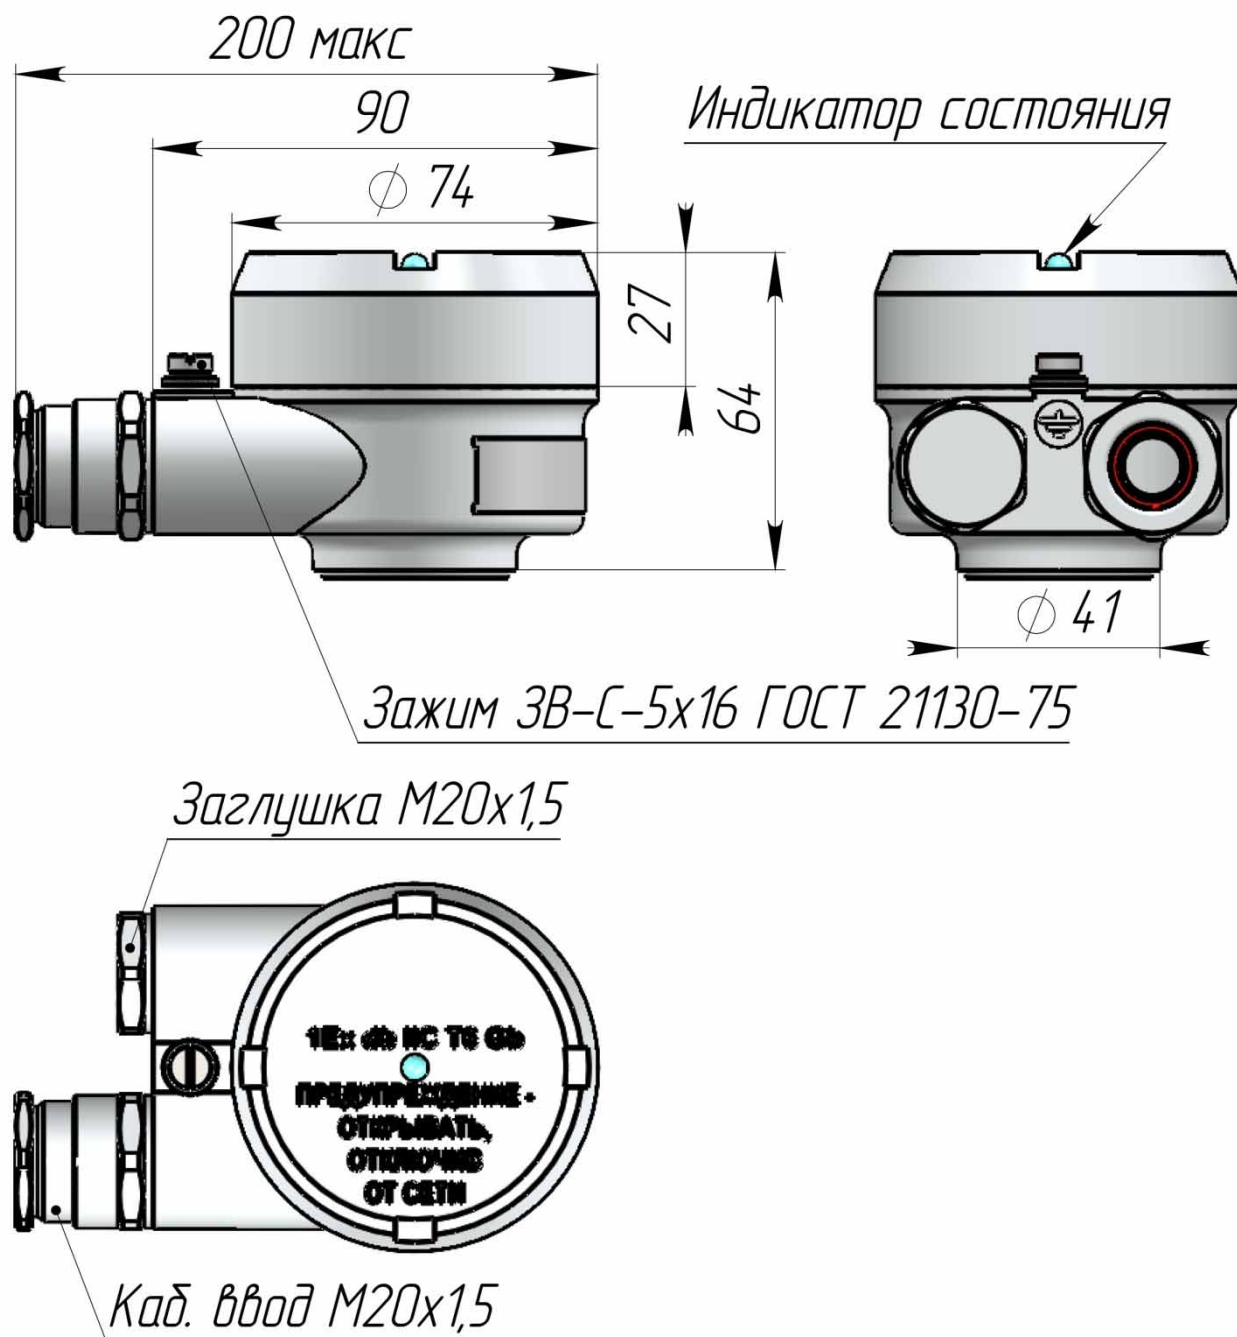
Габаритные размеры корпуса блока электронного в корпусе из нержавеющей стали для общепромышленного применения
